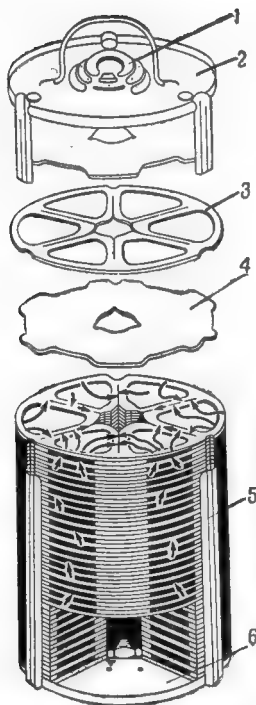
Пластиновый фильтр грубой очистки двигателя ГАЗ-51:
